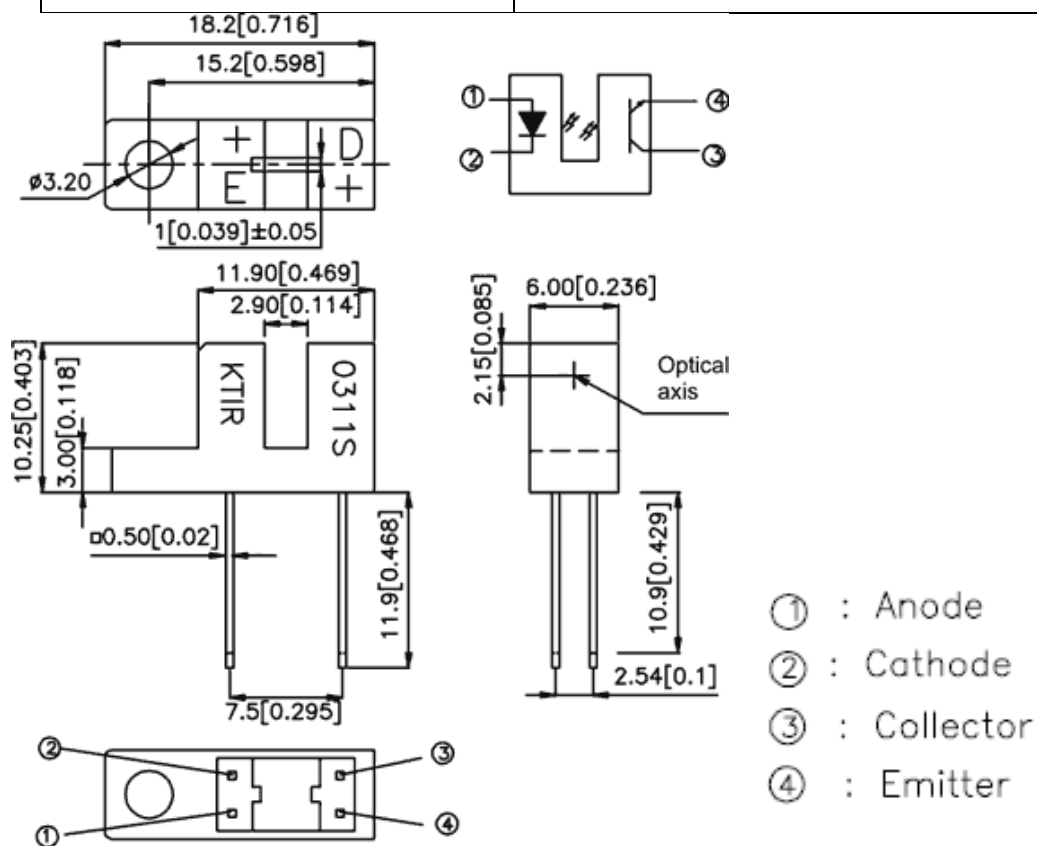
Чертеж габаритных размеров оптрона КТІR0311S
